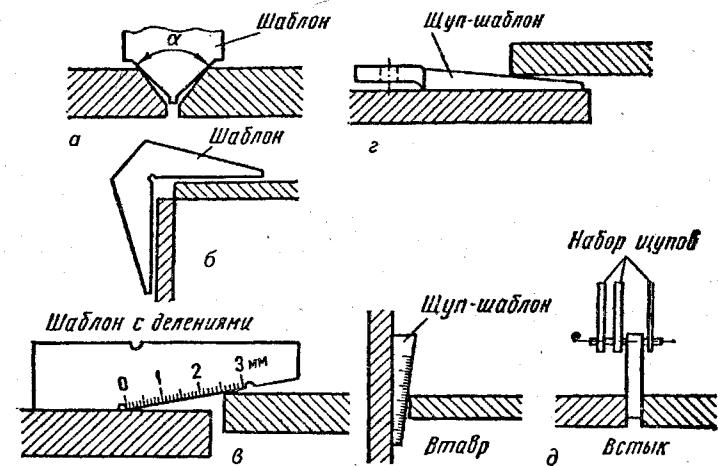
Проверка качества сборки: а — угла раскрытия кромок; б — прямого угла; в — превышения кромок; г — зазора между листами при сварке внахлестку; д — зазора при сварке втавр и встык
